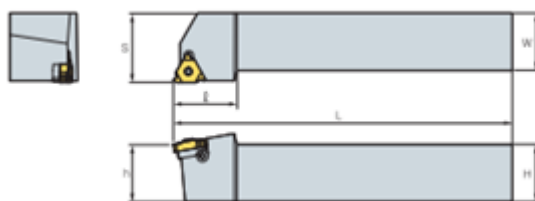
Державка резца для нарезания наружной метрической резьбы
